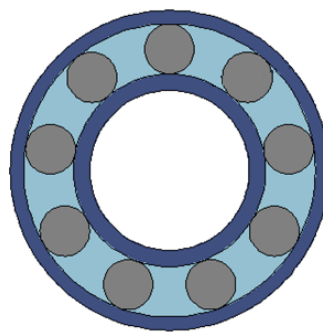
Esquema de rodamiento de 9 rodillos cilíndricos
